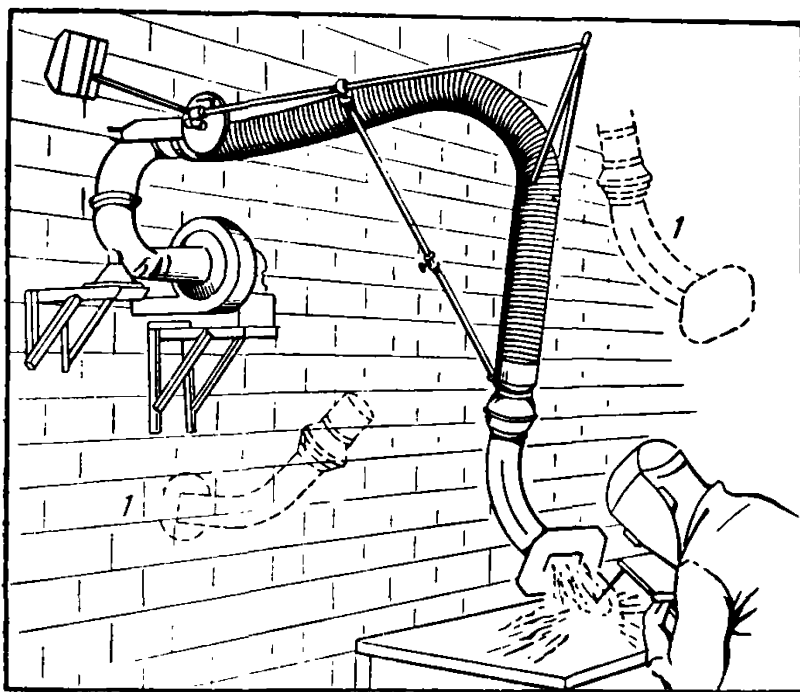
Местная вытяжная вентиляция для отсоса газов при дуговой сварке с помощью подвижной всасывающей головки:
